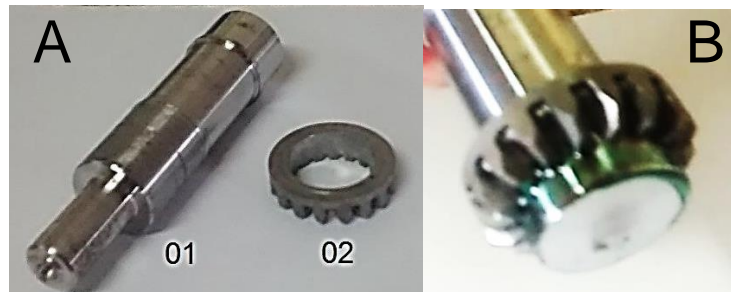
(A) Peças prontas para montagem: (01) Eixo; (02) Engrenagem sinterizada. (B) Engrenagem montada no eixo.
